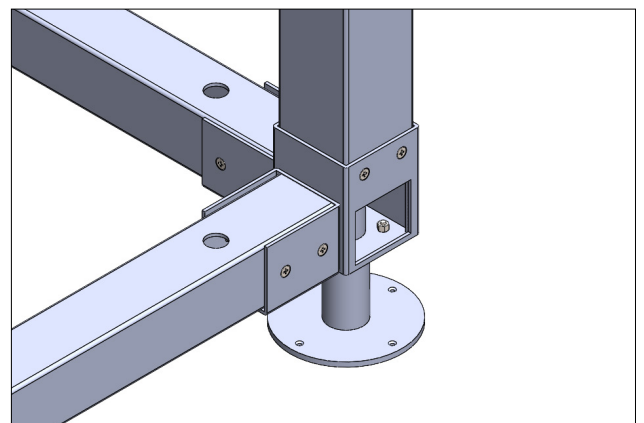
Esquina con las soldaduras y uniones atornilladas.
